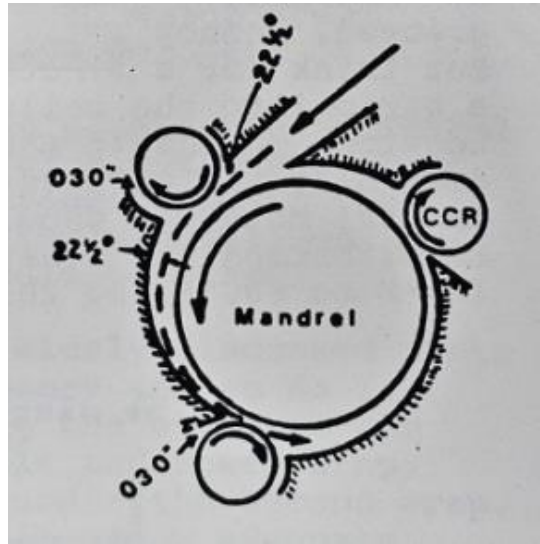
Configuración de enrollador con 3 rodillos unitarios
